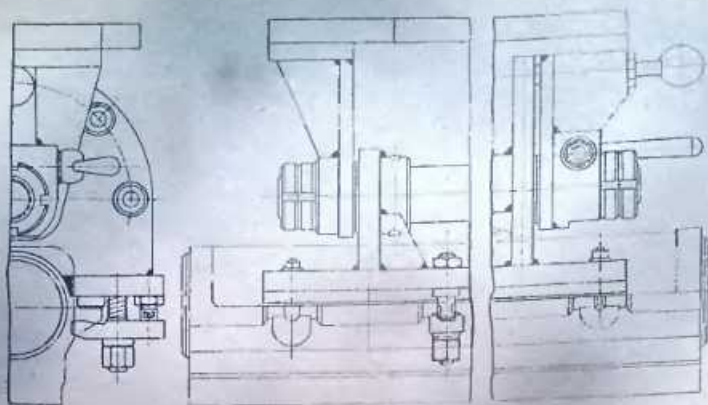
Приспособление ЛМ9690-152 для сборки и разборки топливного насоса
